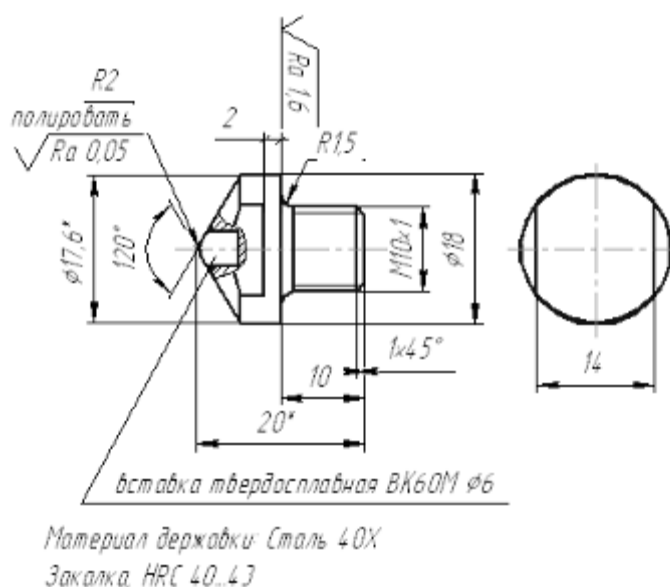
Конструкция инструмента с твердосплавной вставкой
